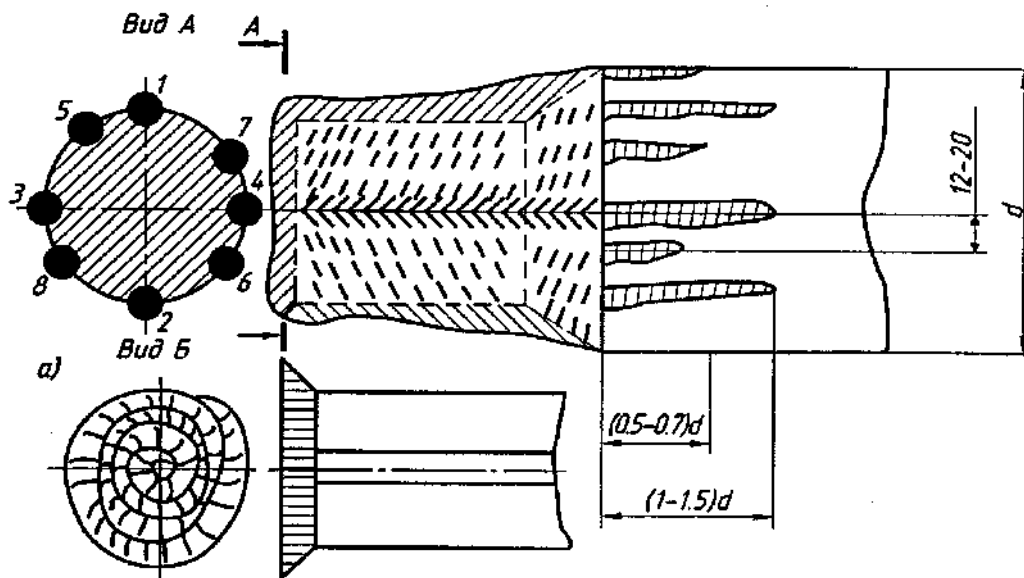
Восстановление посадочной поверхности вала (а) и его торца электродуговой наплавкой (б)
